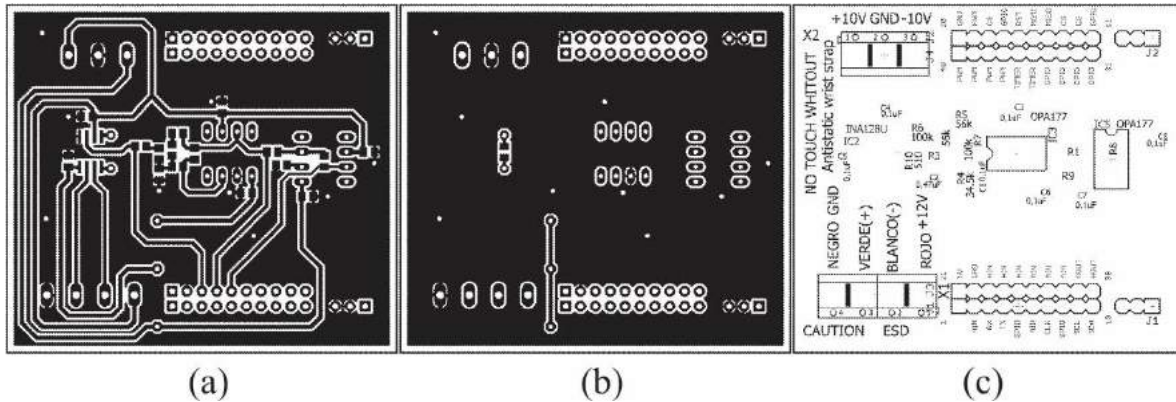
Diseño de la PCB para el acondicionamiento de la celda de carga. (a) capa superior, (b) capa inferior y (c) capa de nombres.
